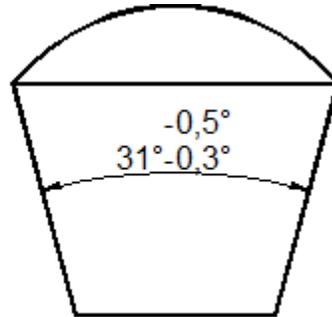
Indicación de la tolerancia dimensional mediante las desviaciones dimensionales.
